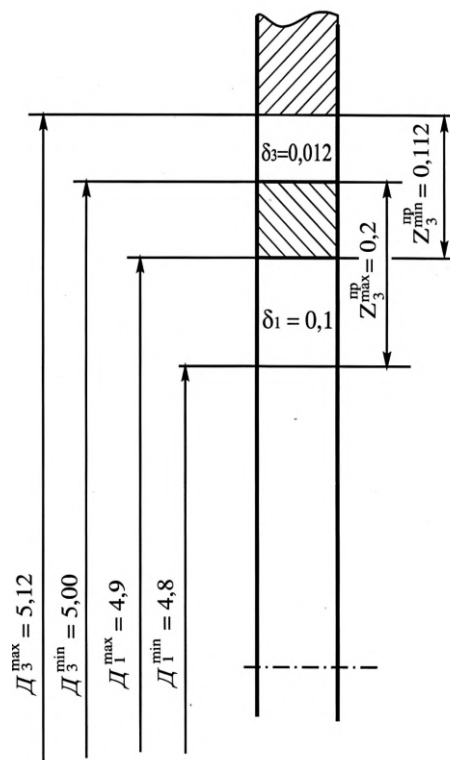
Схема графічного розташування припусків та допусків на обробку поверхні А
